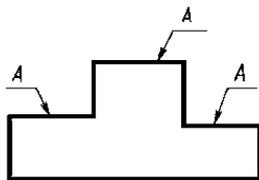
Пример обозначения одинакового покрытия на несколько поверхностей
